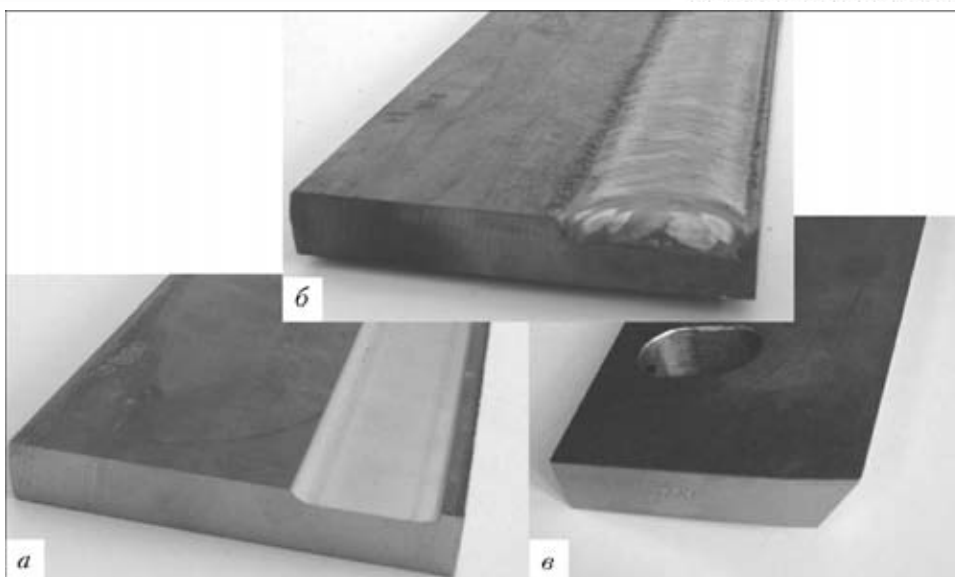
Внешний вид заготовки ножа до наплавки (а), после наплавки (б) и механической обработки (в)
